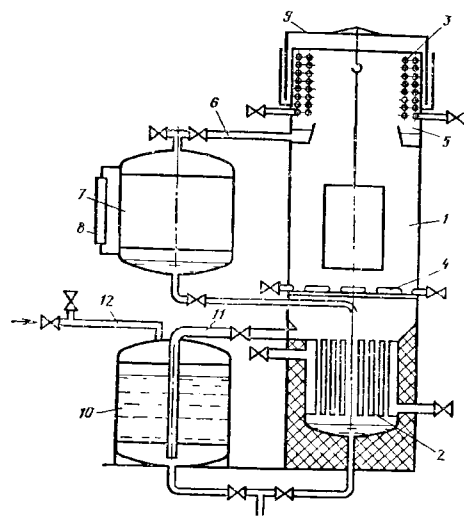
Схема установки для мойки и обезжиривания деталей летучими растворителями
